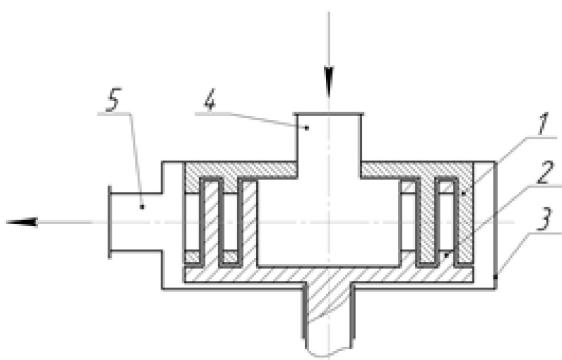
Схема корпусного роторно-пульсаційного апарату: 1 — статор; 2 — ротор; 3 — корпус; 4, 5 — завантажувальний та розвантажувальний патрубки
